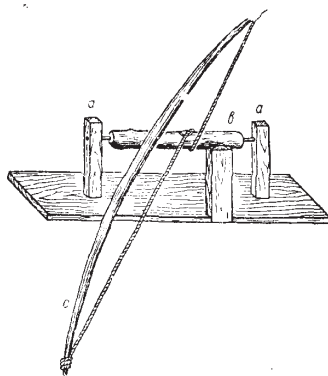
Древний токарный станок с ручным лучковым приводом
